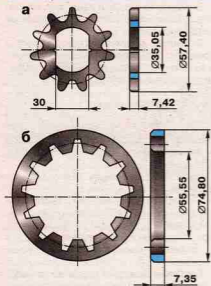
Предельные износы шестерен масляного насоса (размеры диаметров по вершинам зубьев даны для справок): а — ведущей шестерни; б — ведомой шестерни
